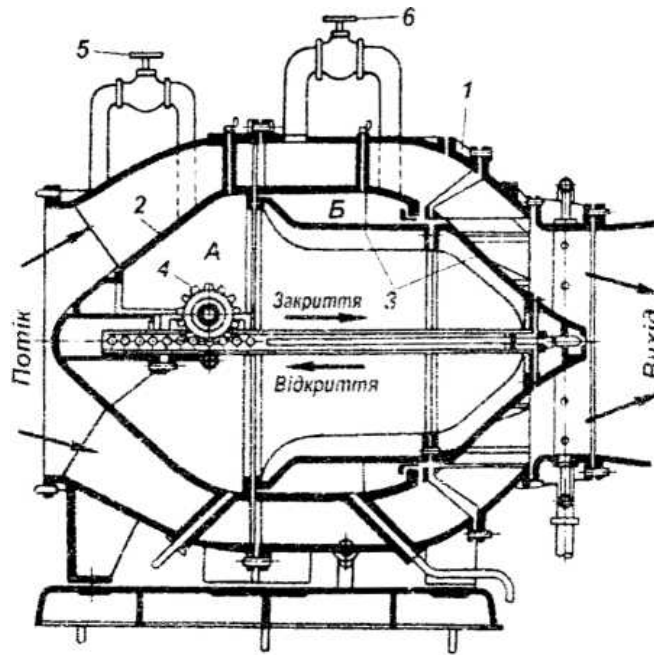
,46 Конструктивна схема голчастого затвора з механічним приводом
